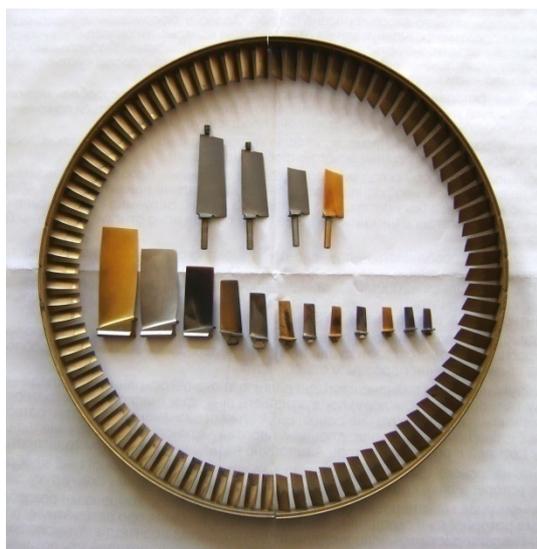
Общий вид лопаток компрессора ГТД модели ТВ3-117
